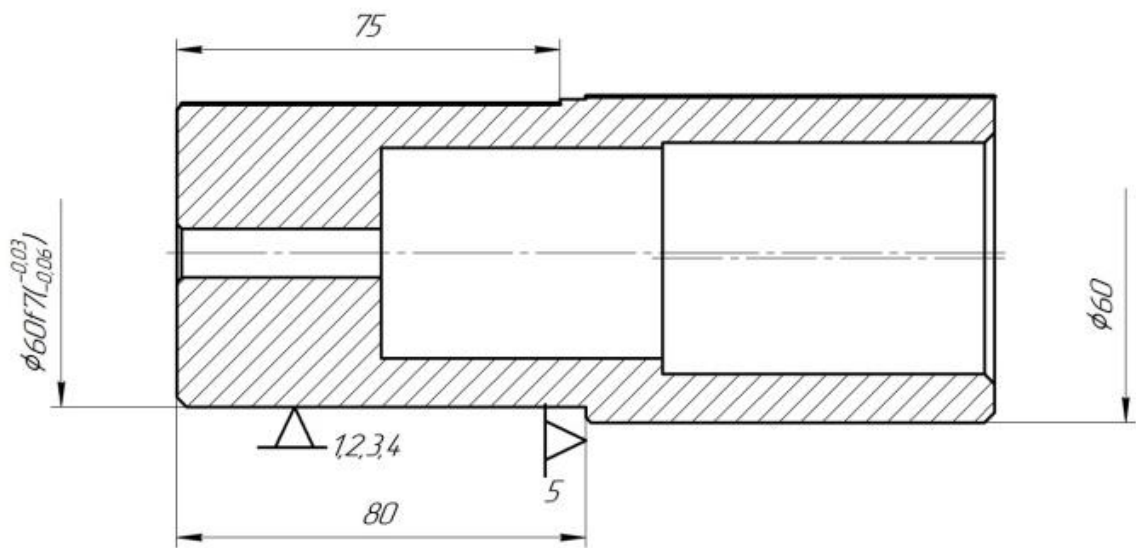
Схема базирования заготовки на фрезерной операции II вариант
